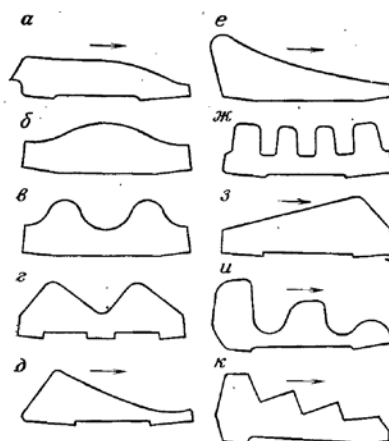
Профили футеровочных плит цилиндрической части барабана стержневых и шаровых мельниц: а – каскадный; б – волновой; в – двухволновой; г – двухугловой; д – Д.К. Крюкова; е – клиновой; ж – ребристый; з – горбатый и – унифицированный норильский; к – каскадно-ступенчатый
